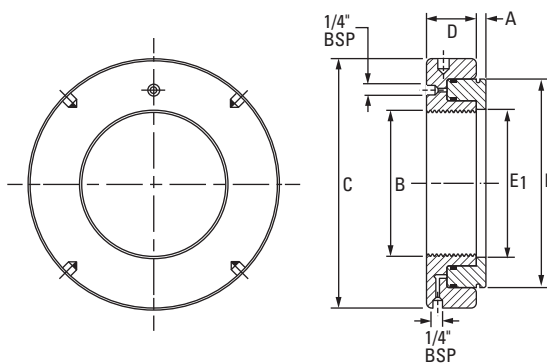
Hydraulická matice používaná k vytažení stahovacího pouzdra
